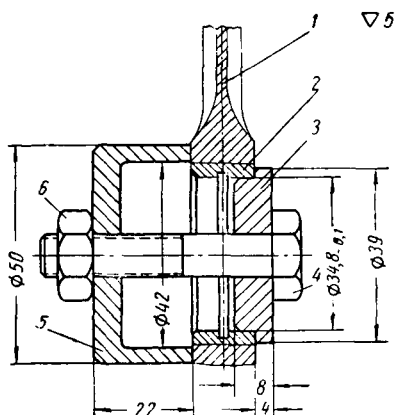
Приспособление для выпрессовки обоймы подшипника из шатуна двигателя мотороллера Т-200М:
